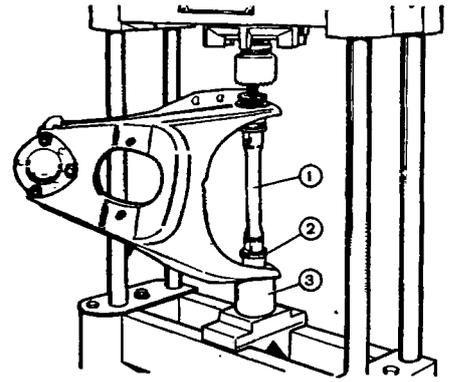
Выпрессовка шарниров нижнего рычага: 1 - ось рычага; 2 - шарнир рычага; 3 - оправка
